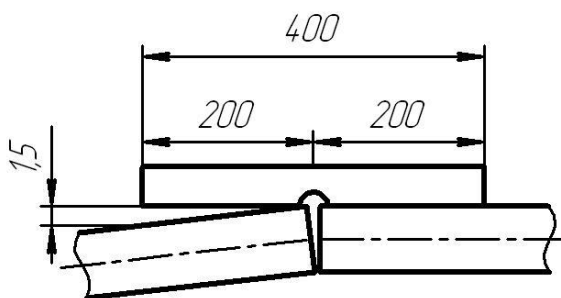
Проверка прямолинейности стыка элементов перед сваркой
